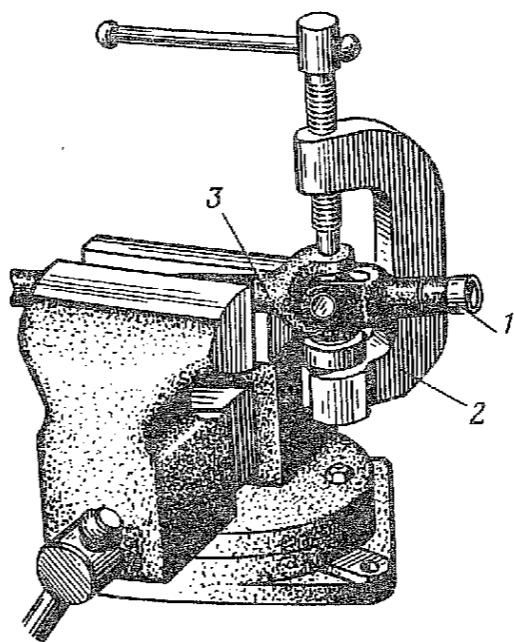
Выпрессовка игольчатого подшипника карданного вала рулевого управления:
